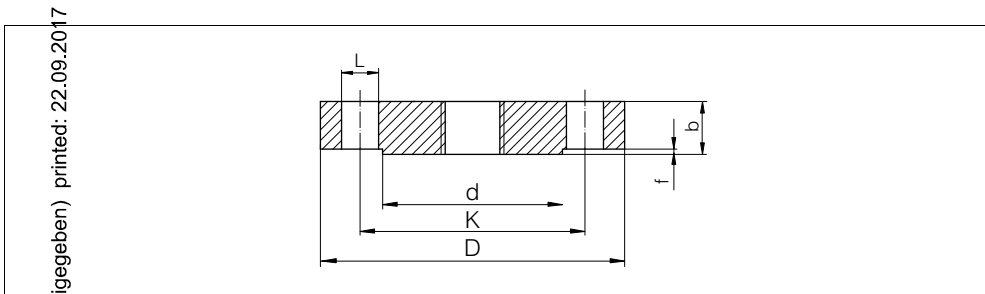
Encombrement - Bride JIS (Regular Flange)
